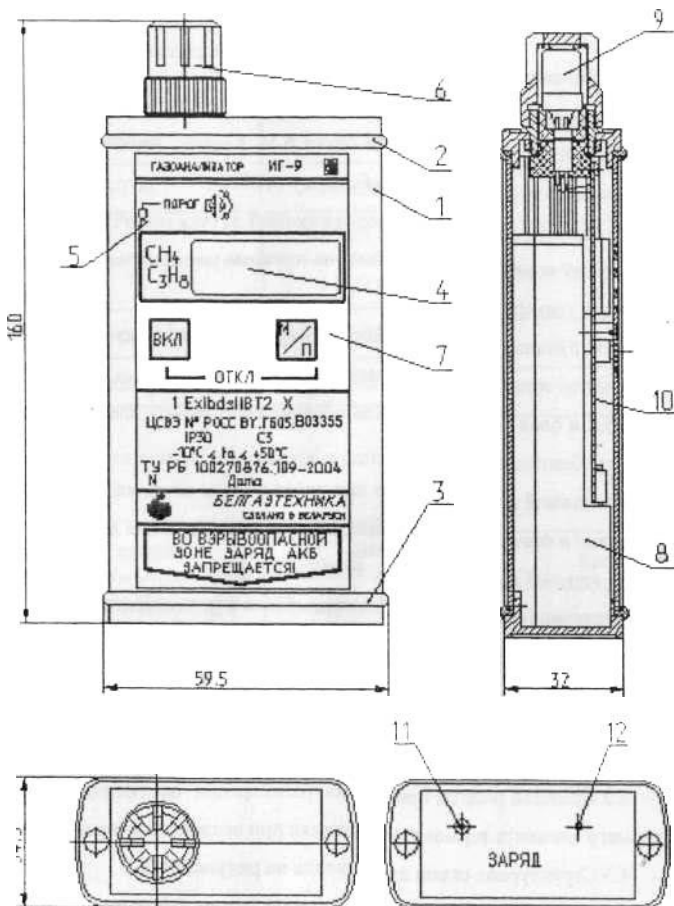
Внешний вид газоанализатора: 1 – корпус; 2 – верхняя крышка; 3 – нижняя крышка; 4 – индикатор; 5 – светодиод «ПОРОГ»; 6 – защитный колпачок датчика; 7 – кнопка; 8 – блок питания; 9 – датчик газа; 10 – плата обработки; 11 – разъем для заряда аккумуляторной батареи; 12 – светодиод индикации процесса заряда
